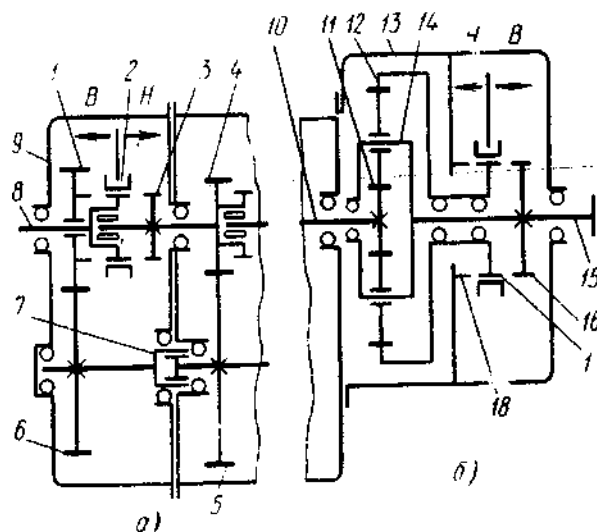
Схемы двухступенчатых дополнительных коробок передач: а — делитель; б — демультипликатор.
